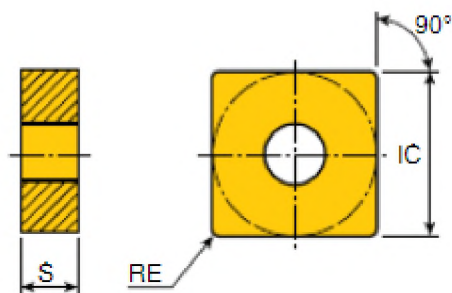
Пластина SNMG120408 FC. CVD покриття : TT8125B
